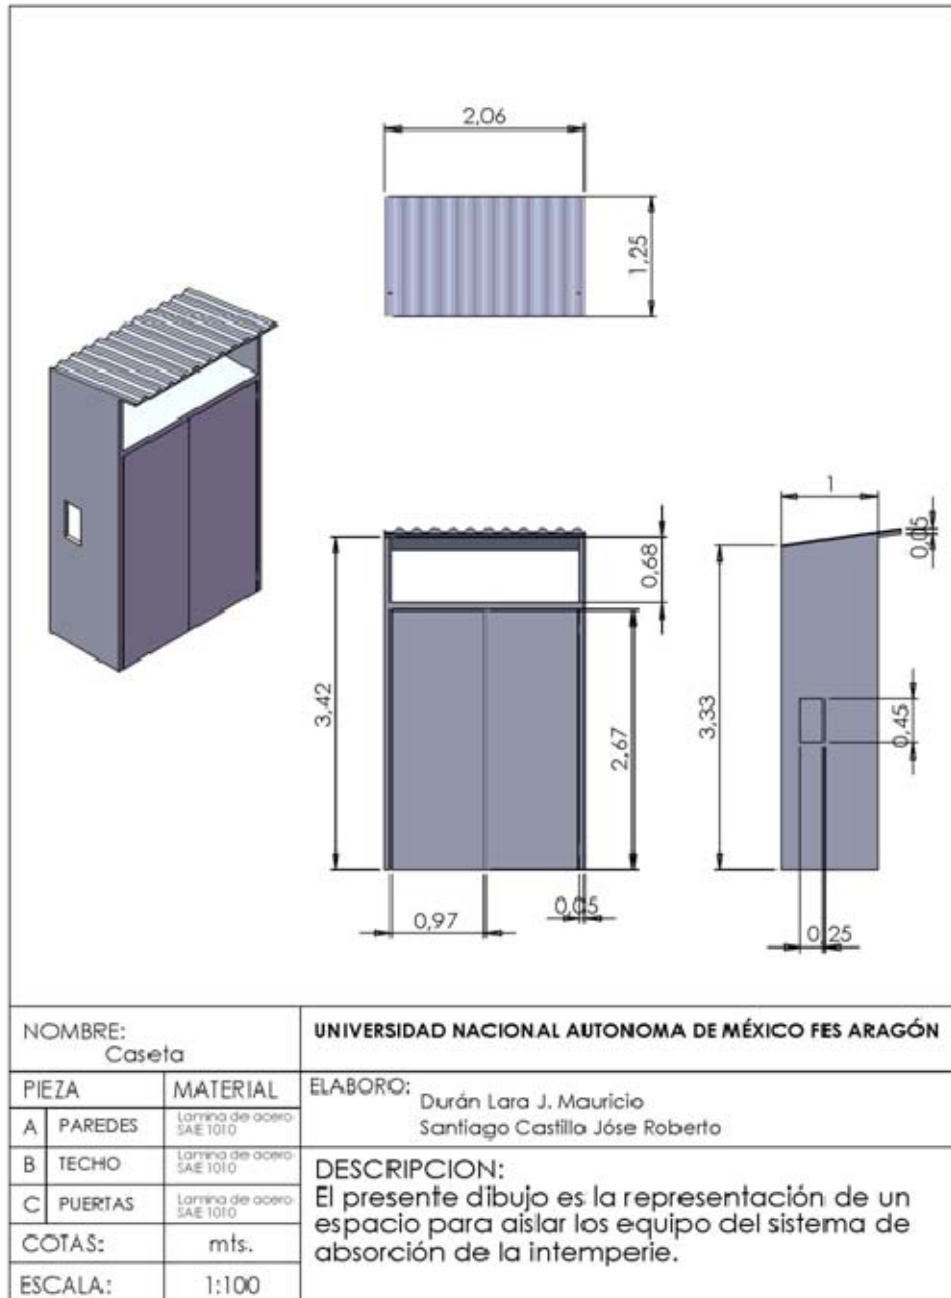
Dibujo técnico de la caseta de resguardo realizada en paquetería CAD.
